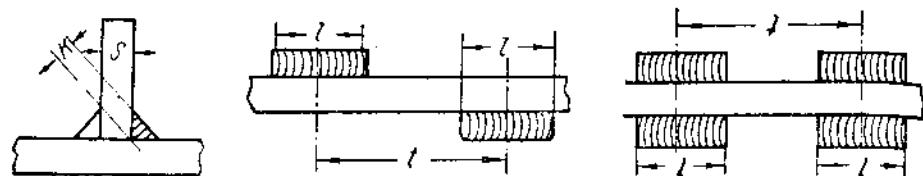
и 121. Образцы для прерывистой валиковой сварки.
